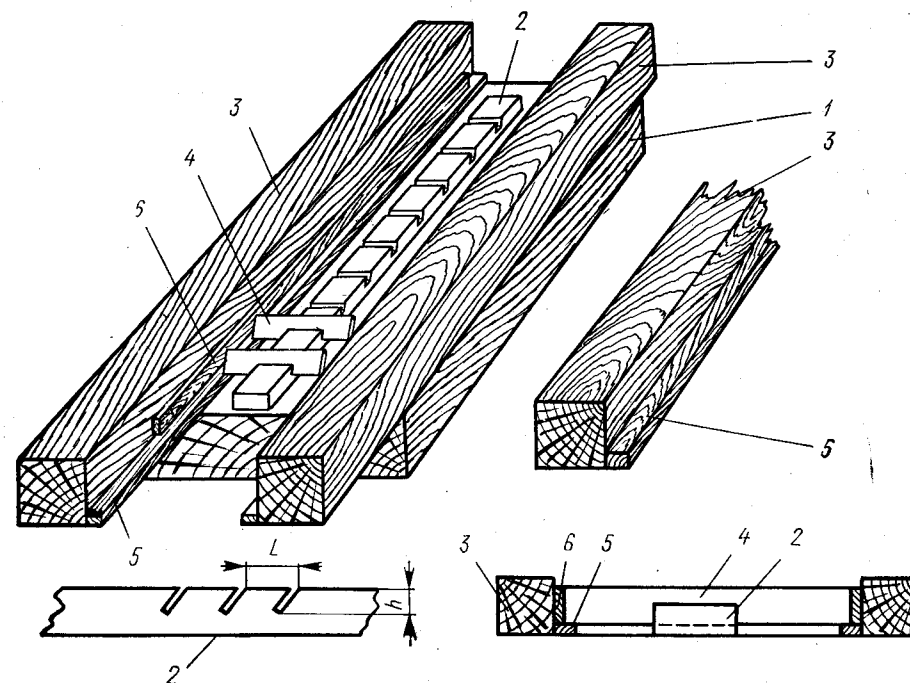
Шаблон-кондуктор для сборки внутренних трапов:
